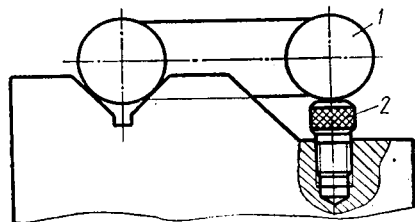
Установка заготовки детали с параллельными осями цилиндрических поверхностей
